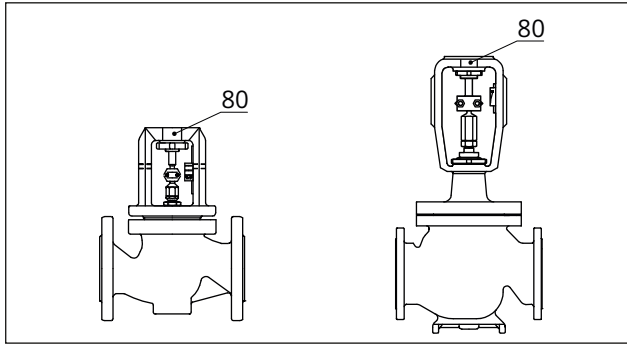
Flanş üzerindeki isim etiketi (solda) · Yoke bağlantısı üzerindeki isim etiketi (sağda)
